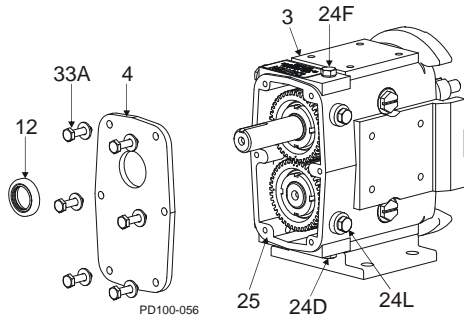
Abnehmen des Getriebegehäusedeckels
